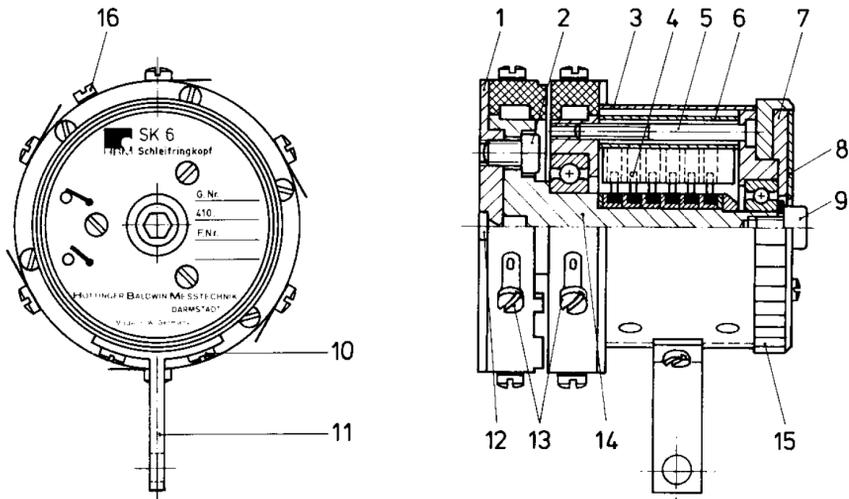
Schleifringkopf SK6: 1 = Montageplatte; 2 = Befestigungsschraube; 3 = Gehäuserohr; 4 = Bürstenhalter; 5 = Distanzbolzen; 6 = Distanzhülse; 7 = Stirnplatte; 8 = Typenschild; 9 = Sicherungsschraube; 10 = Befestigungsschrauben für Montagewinkel; 11 = Montagewinkel; 12 = Kabelführungsnuten; 13 = Lötösen; 14 = Rotor; 15 = Stelling; 16 = Statormasse; aus: /2/
